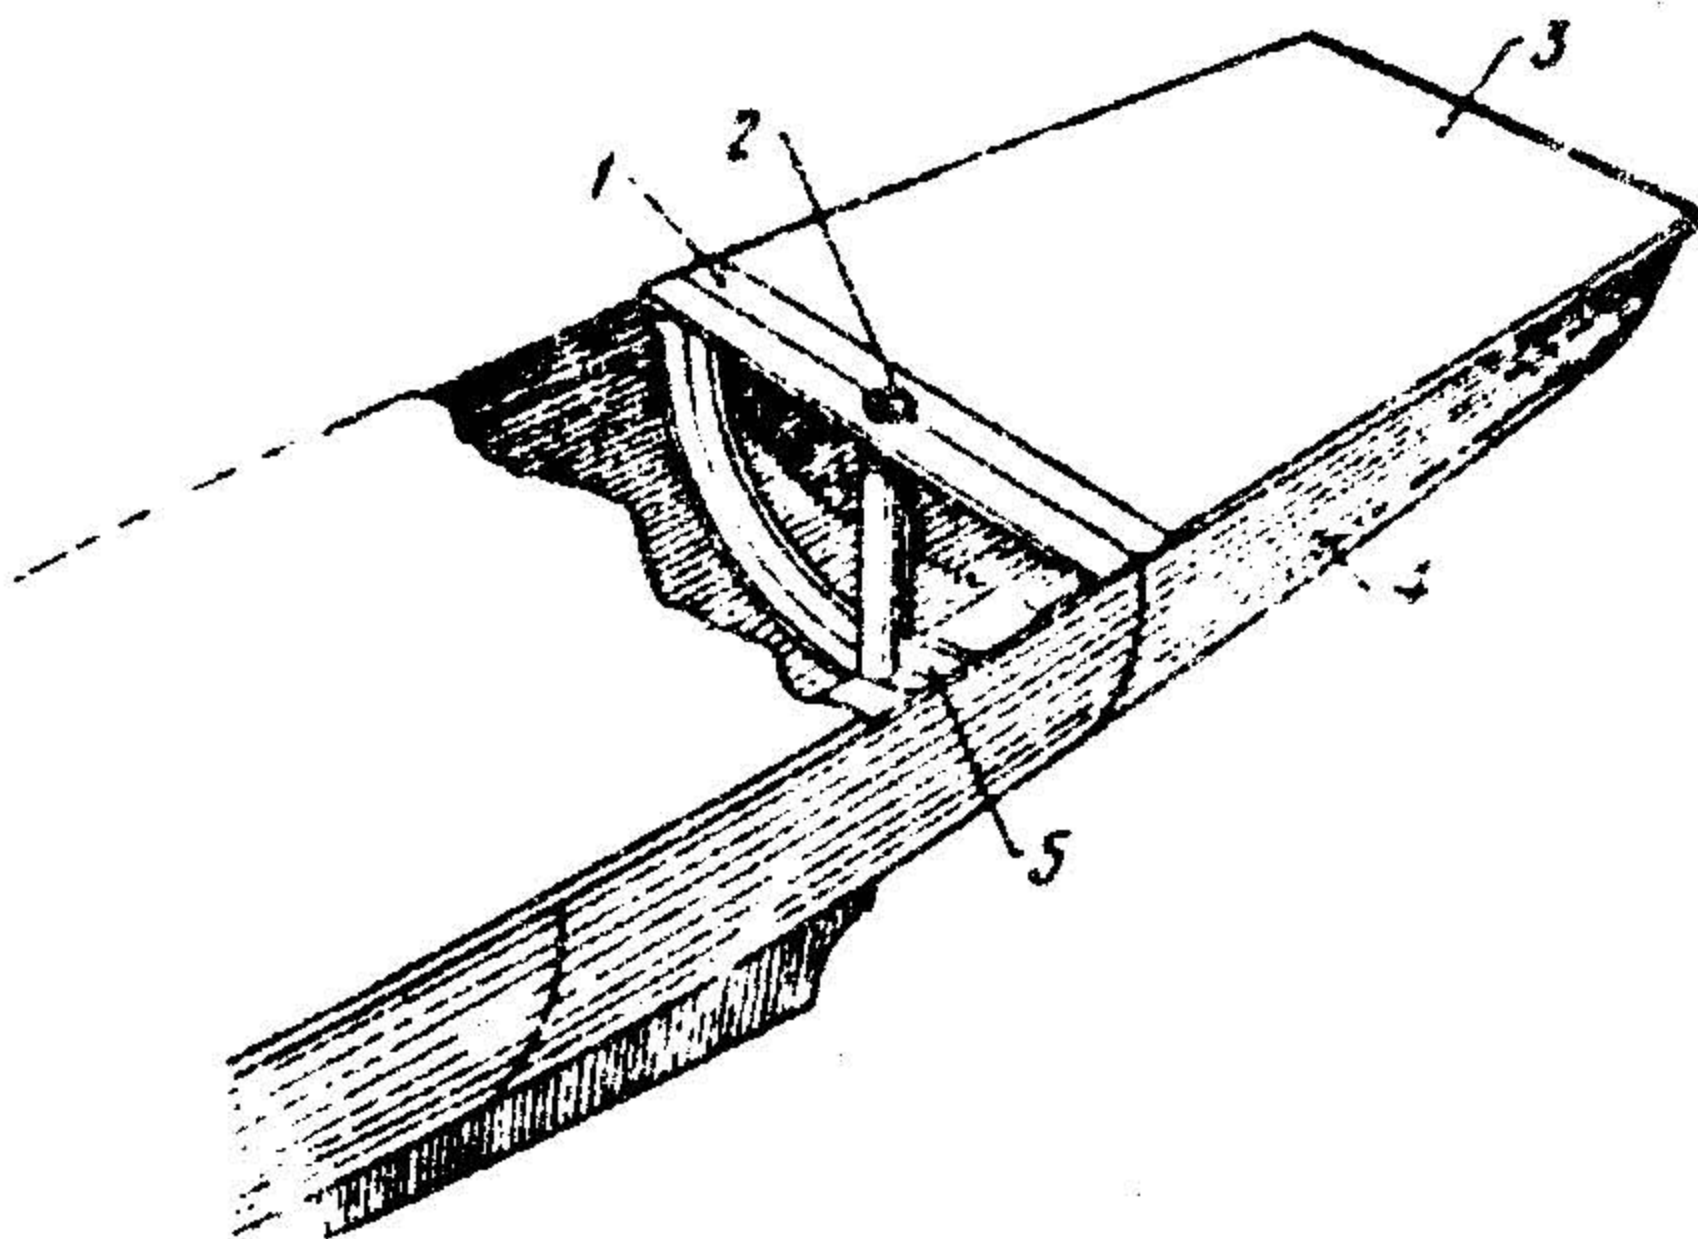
Крепление гельмпортной трубки: 1 — бимс; 2 — гельмпортная трубка; 3 — часть палубы; 4 — обшивка; 5 — шпангоут
